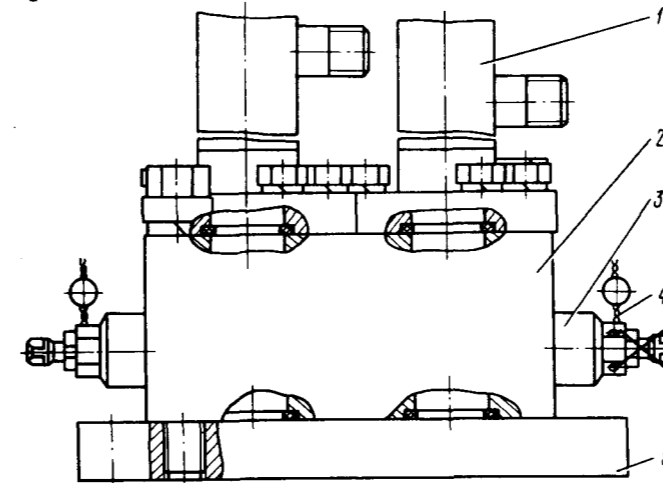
Блок перепускных клапанов: I - труба; 2 - корпус; 3 - клапан предохранительный; 4 - пломба; 5 - плита
